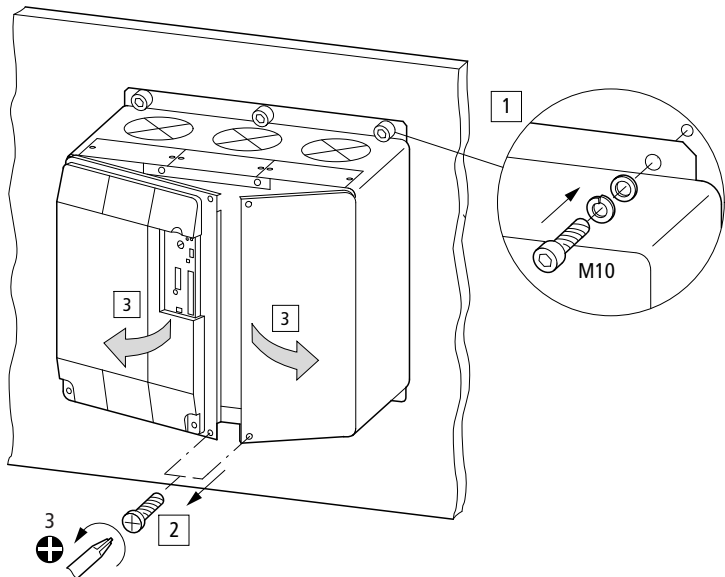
Befestigung auf Montageplatte DM4-340-250K bis DM4-340-500K
